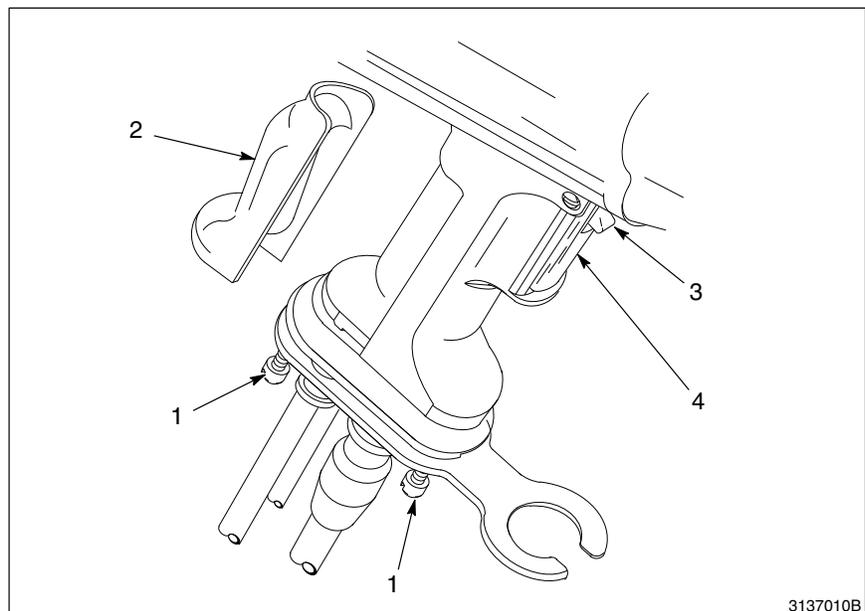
Poudrage, purge et changement de bourrelet de la poignée
